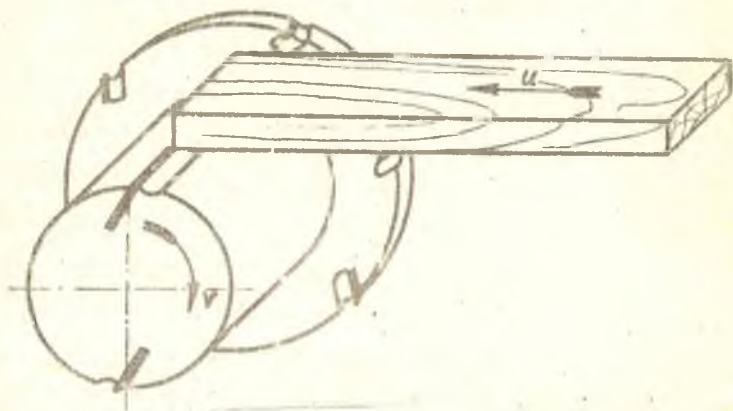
Рис. I. Схема обработки заготовки комбинированным режущим инструментом.
